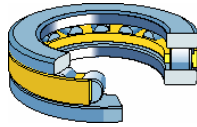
Rodamiento axial de rodillos cilíndricos [28].
